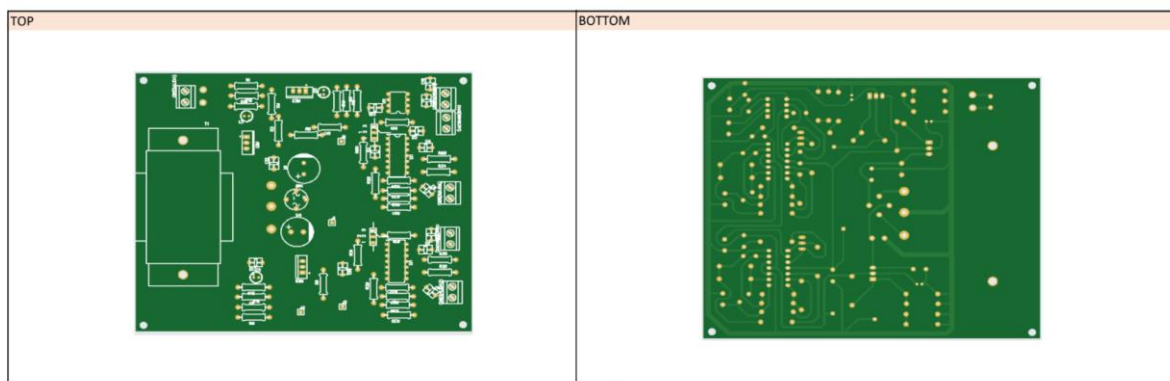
Propuesta técnica de la PCB (UNIT Electronics, 2025)
